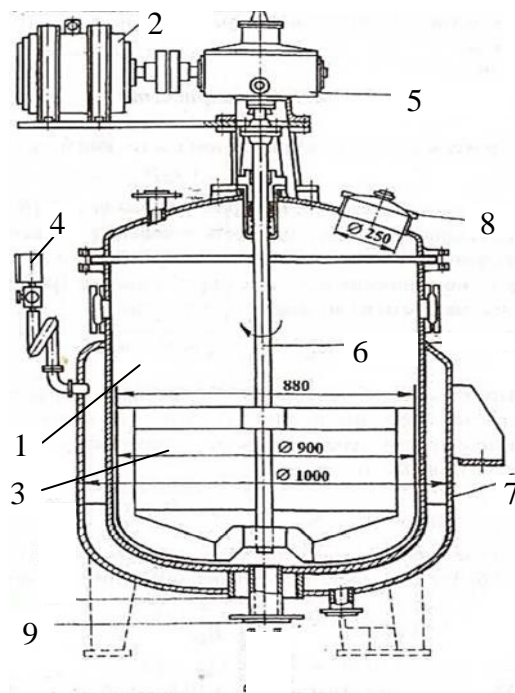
Конструктивна схема механічного змішувача компонентів: 1 – робоча камера; 2 – приводний механізм; 3 – диски; 4 – пристрій для подачі рідких (рідинних) інгредієнтів; 5 – пристрій подачі сипкого компонента; 6 – приводний вал; 7 – мішалка; 8 – горловина; 9 – вивантажувальний канал
